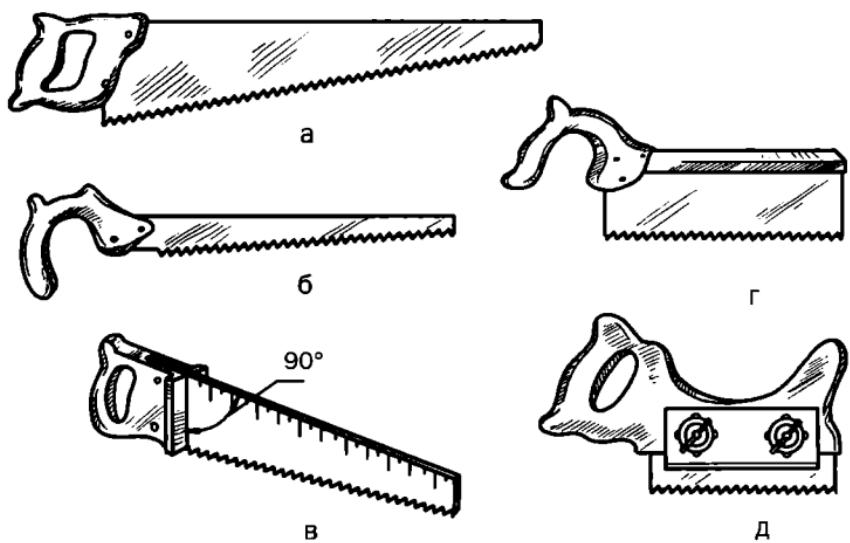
Ножовки: а — широкая; б — узкая; в — измеритель; г — с обушком; д — наградка
